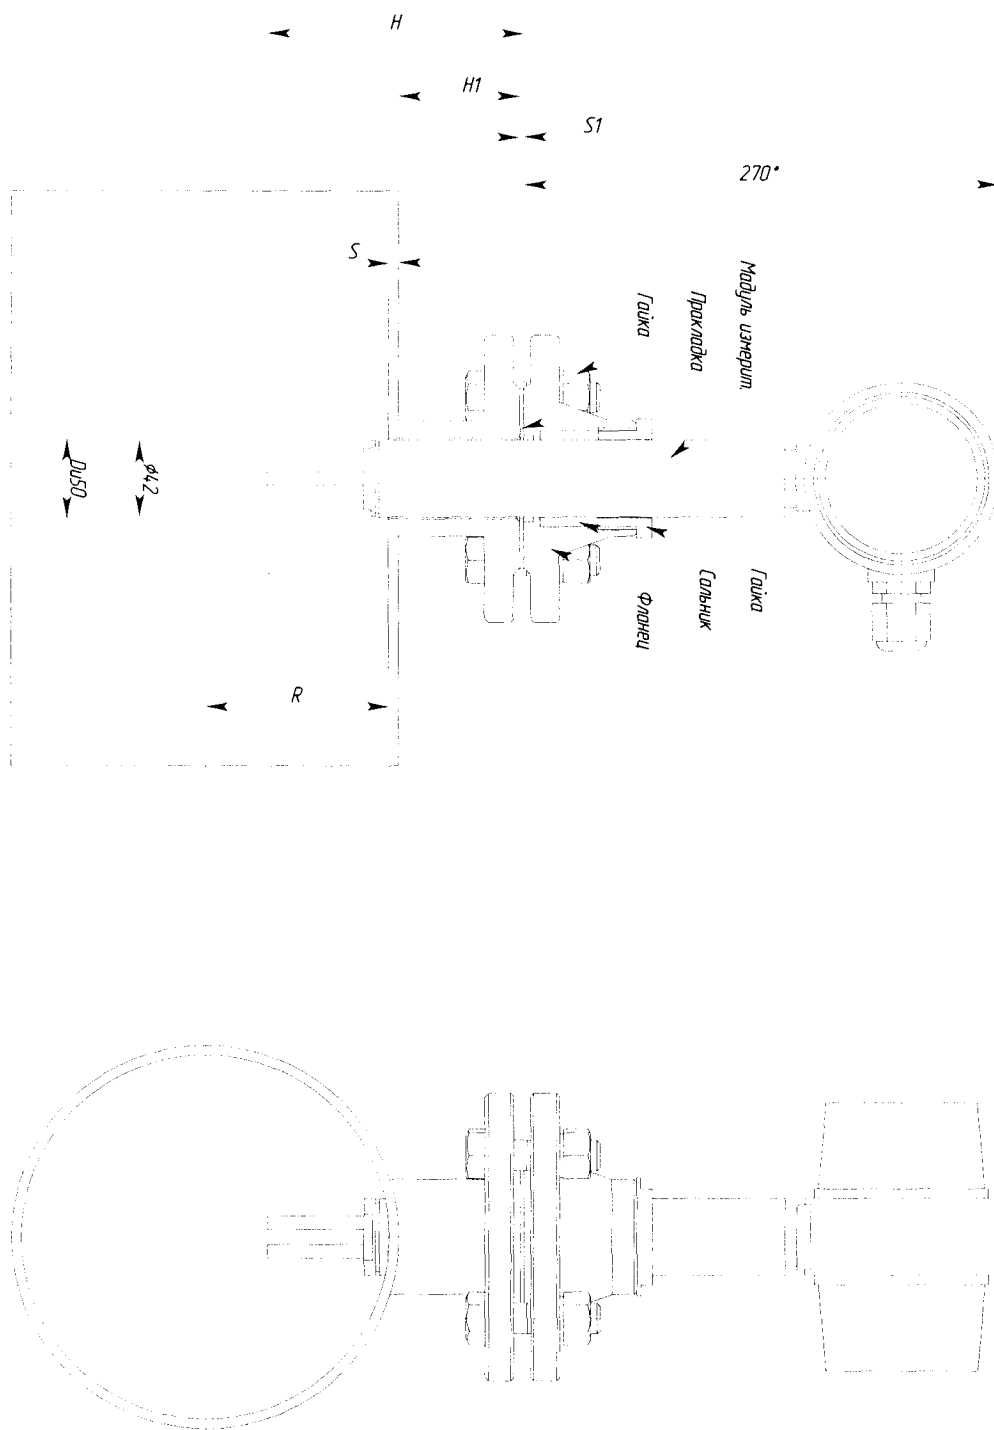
Схема монтажа МИ с сальниковым уплотнением
